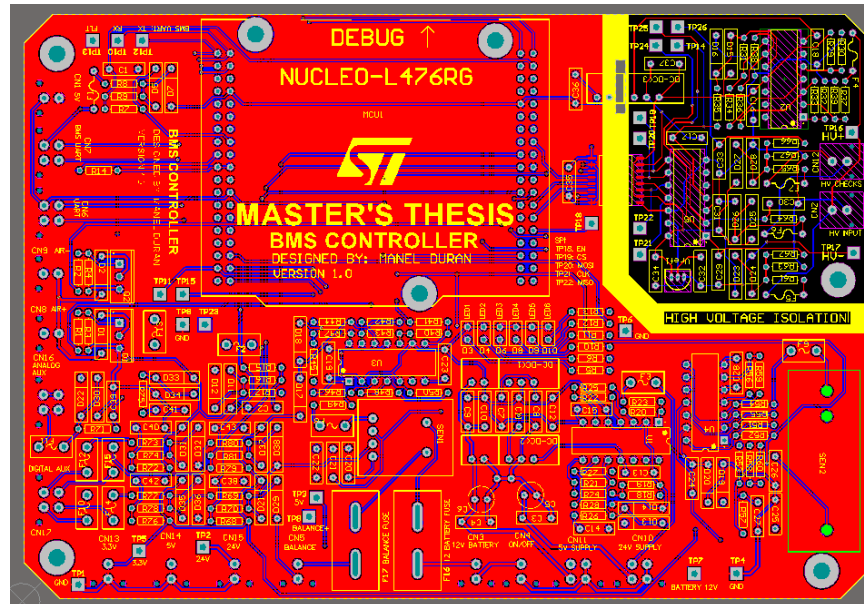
PCB enrutada i amb el pla de massa de la capa superior.
